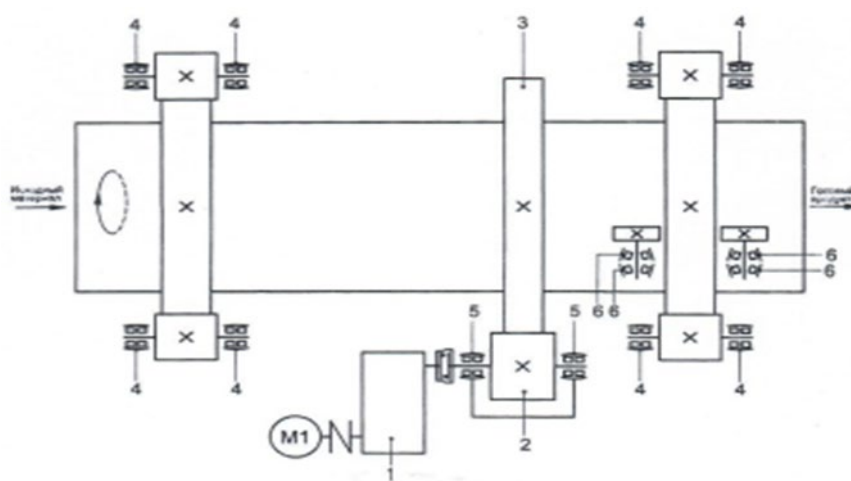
Кинематическая схема смесителя-окомкователя барабанного Ø2,8×8 м:
